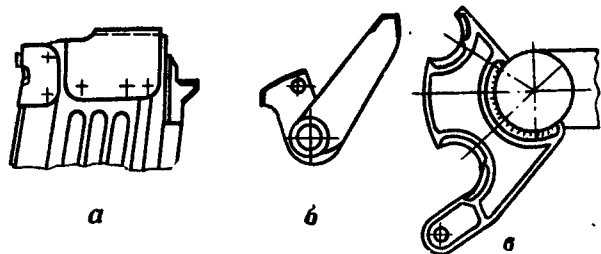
Примеры наплавки поверхностей деталей стрелкового оружия:
